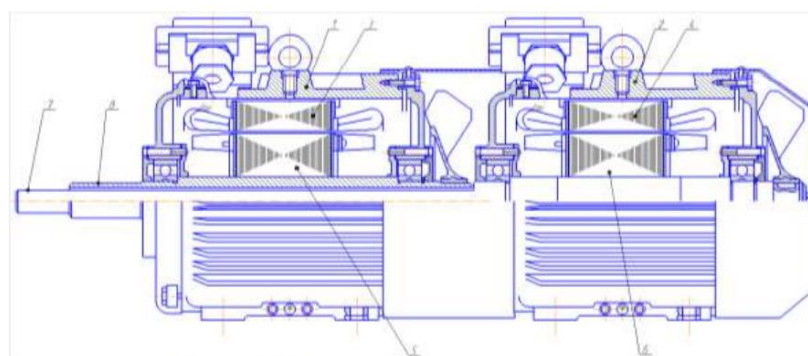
Общий вид сдвоенного электродвигателя 1, 3 – корпус; 3, 4 - статор; 5, 6- ротор; 7, 8 - соосные валы
